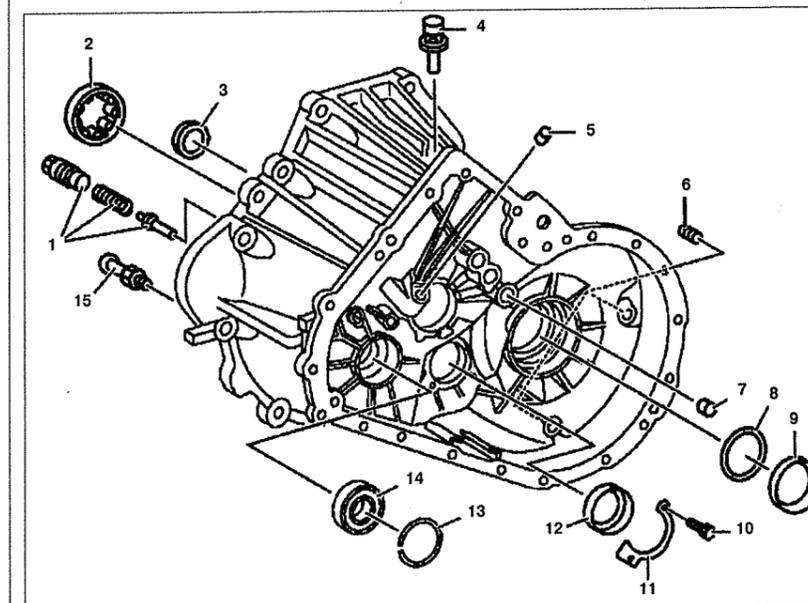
Корпус сцепления (автомобили с двигателями 111.948 и 601.970):
